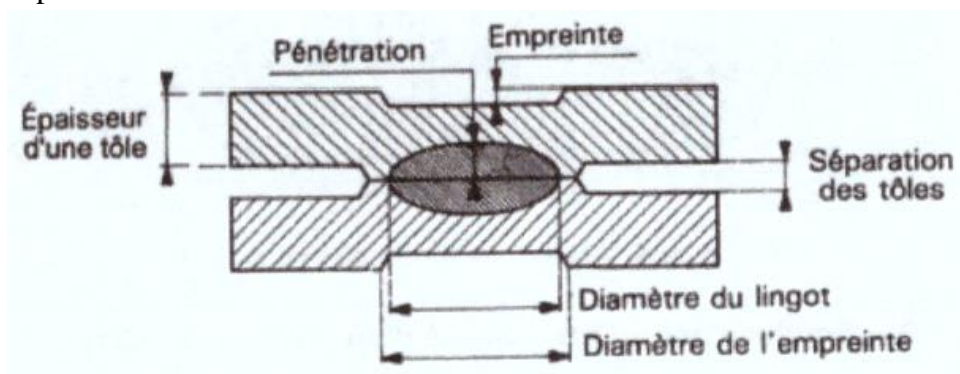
Soudage par points : caractéristiques dimensionnelles d'un point de soudure
